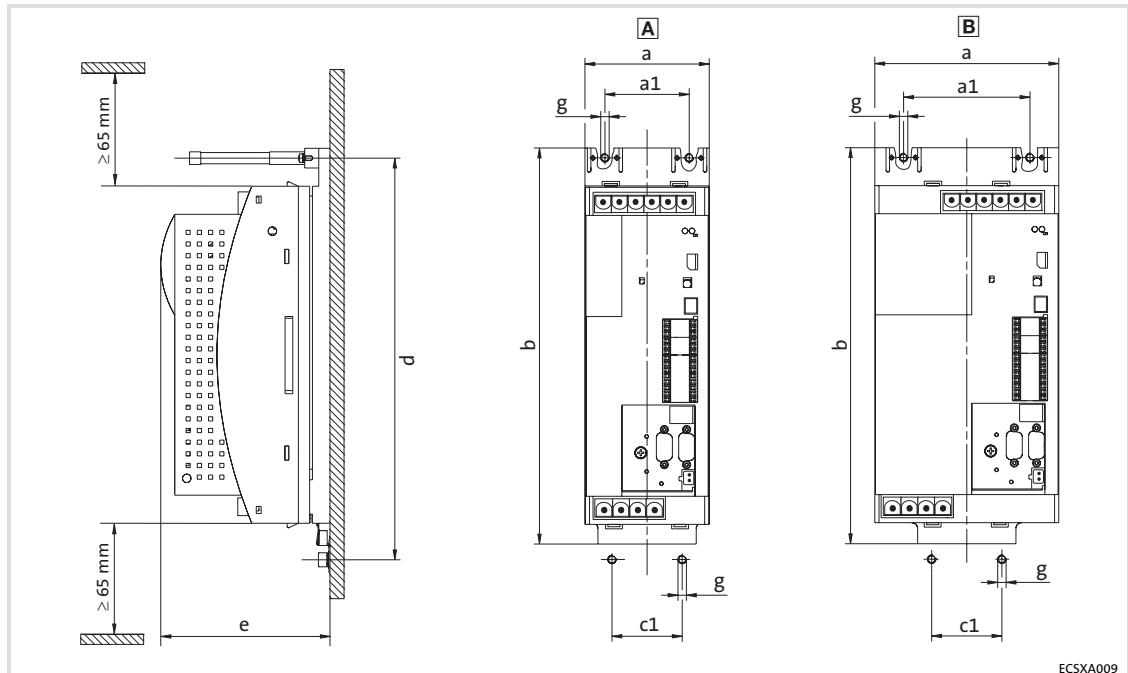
Dimensiones para el formato "Técnica Cold Plate"
